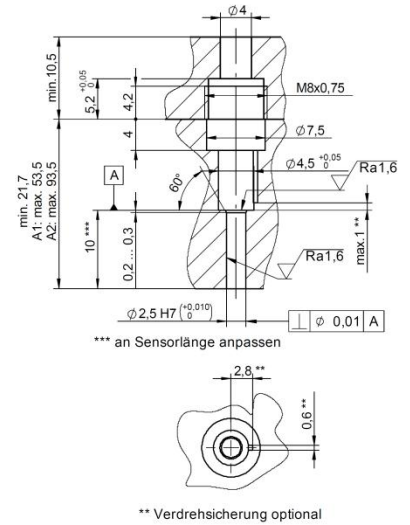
Montagebohrung für Einbau mit ladungsführender Distanzhülse
